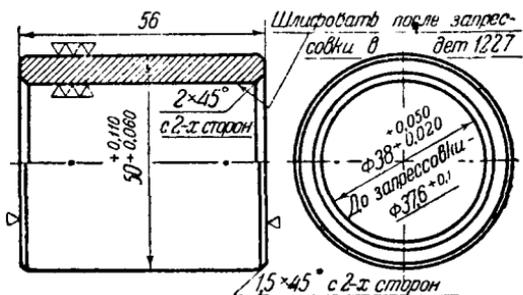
Дет. № 1230. Втулка шестерни заднего хода
